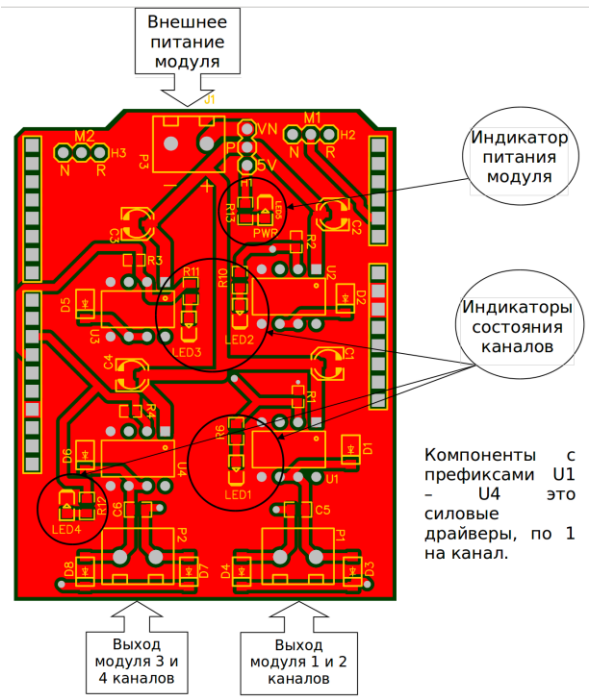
внешний вид полученной платы с шелкографией для упрощения ручной пайки
